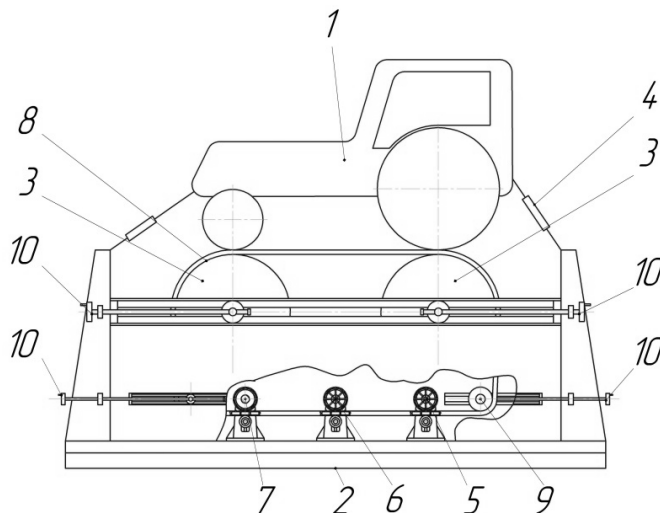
Стенд для моделювання нерівностей дорожнього полотна: 1-випробувальна машина; 2 - станина; 3 – опорні барабани; 4 – натяжники; 5 – механізм спускання; 6 – механізм накачування; 7 – аналізатор; 8 – нескінченна стрічка з камерами для повітря; 9 – натяжні ролики; 10 – натяжні пристрої.
